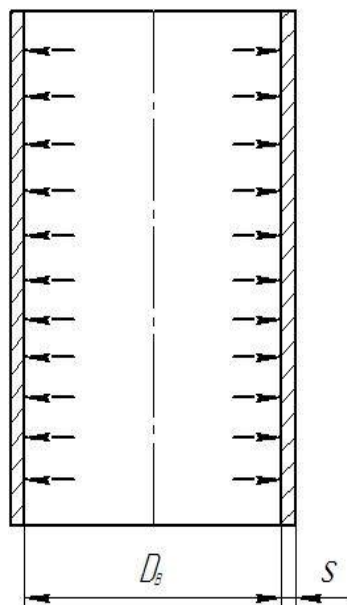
Розрахункова схема обичайки корпусу, навантаженого внутрішнім тиском
